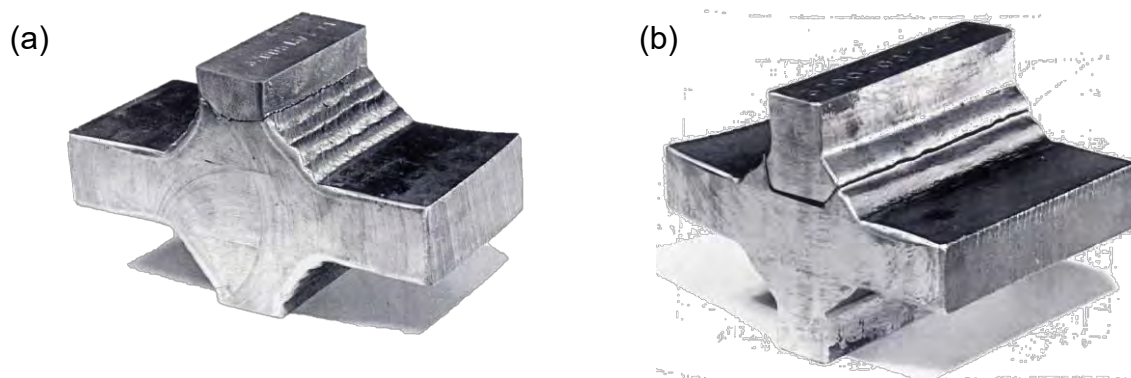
Kreuzstoß-Probekörper mit Ermüdungsriss ausgehend vom Schweißnahtübergang (a) sowie von der Schweißnahtwurzel (b) [#60]
